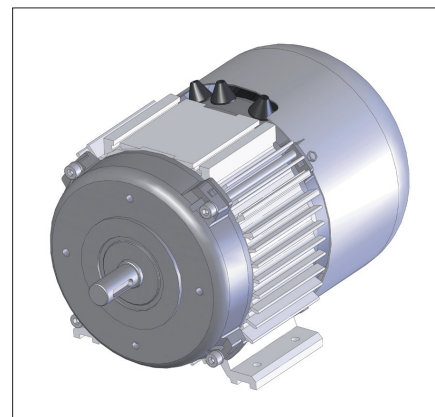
Integrace elektronické jednotky do motoru BLDC
